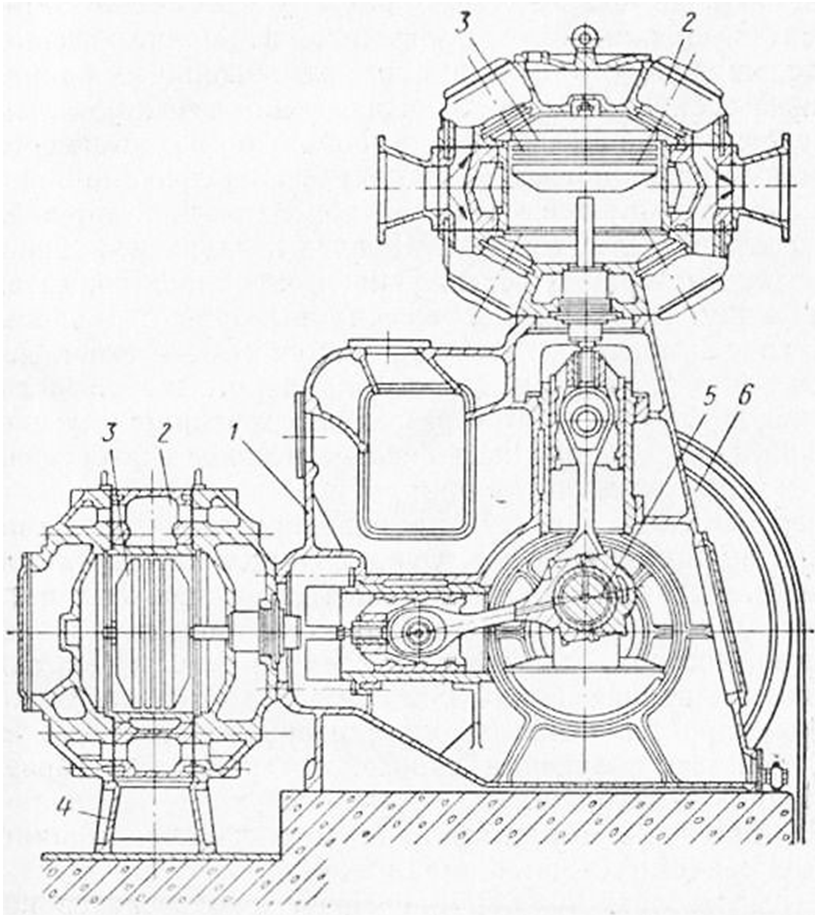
Кутовий компресор з прямокутним розташуванням осей циліндрів 1 - рама-картер; 2 - циліндр; 3 - поршень; 4 - опора; 5 - колінчастий вал; 6 - електродвигун
